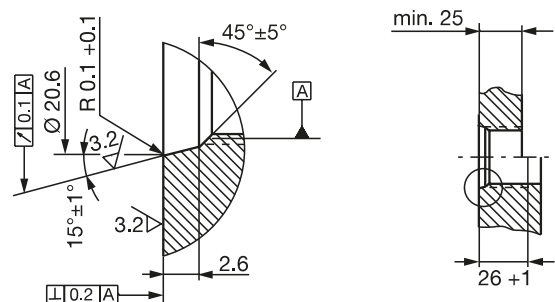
Einschraubloch 3/4"-16UNF nach SAE J475 O-Ring 15.3x2.4
